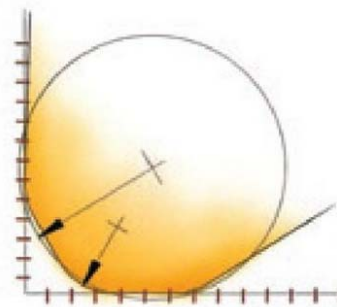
Схема вершины режущей части по технологии Wiper [6]
